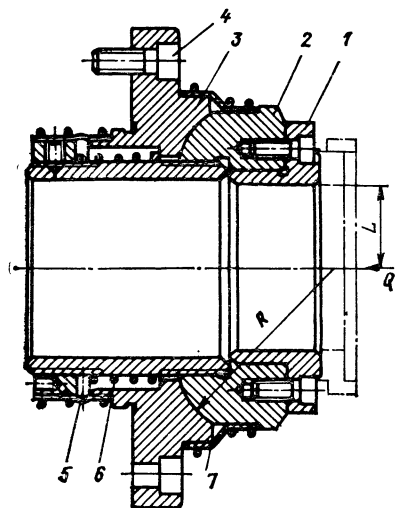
Приспособление с самоустанавливающейся сферической опорой для протягивания отверстий в детали с необработанным торцом
